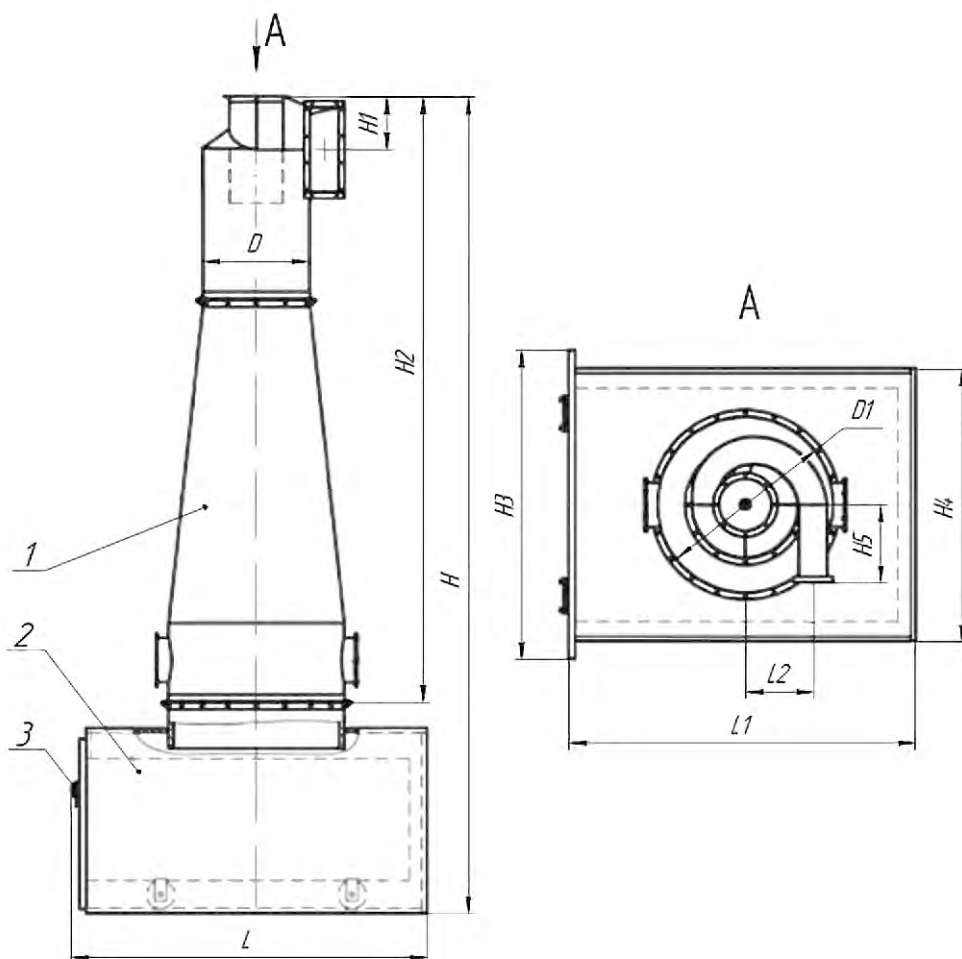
Габаритные и присоединительные размеры циклона ЦМ на пылесборнике.
